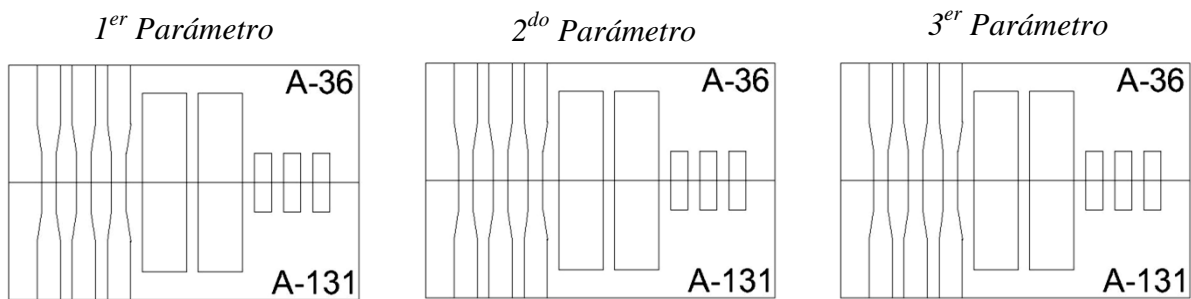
Uniones soldadas de aceros disímiles a diferentes parámetros de soldadura.
